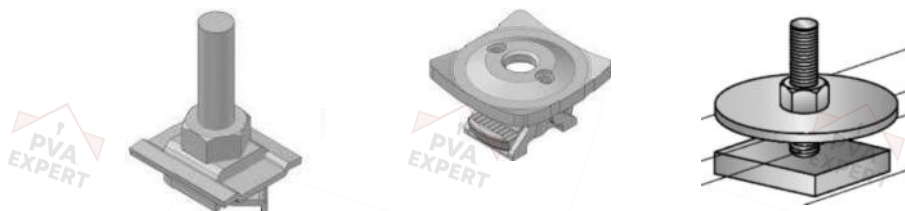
Примеры монтажных гаек для крепления хомутов
